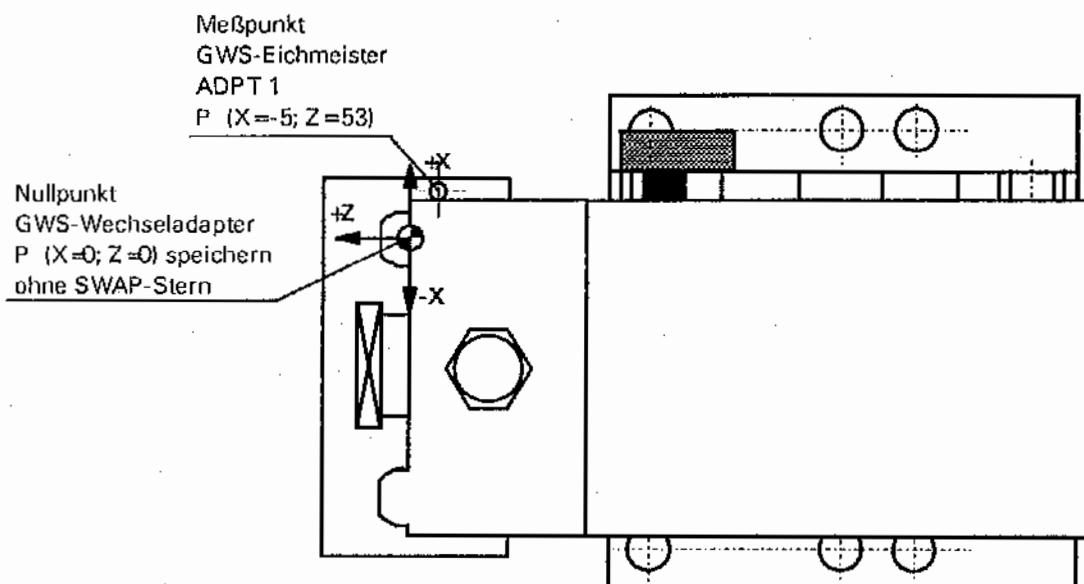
Nullpunkt am GWS-Wechseladapter für Längsschlittenwerkzeuge
